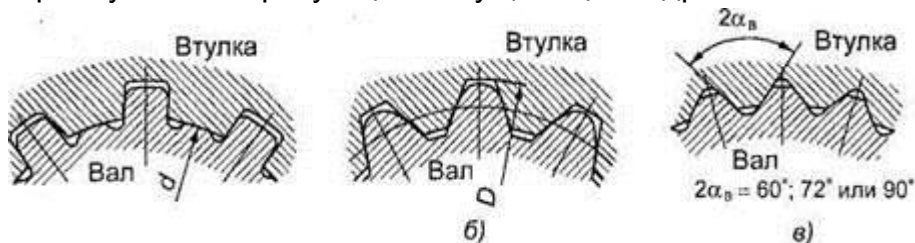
Типы зубчатых (шлицевых) соединений: а — прямобочные зубья; б — эвольвентные зубья; в — треугольные зубья
